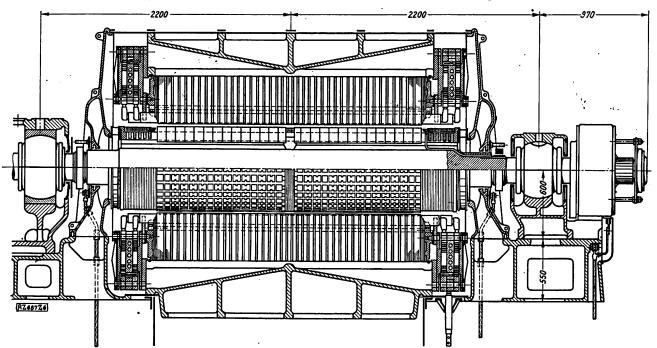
Drehstromerzeuger für 12500 kVA bei 3000 Uml./min, gekuppelt mit der Vorwärmturbine
